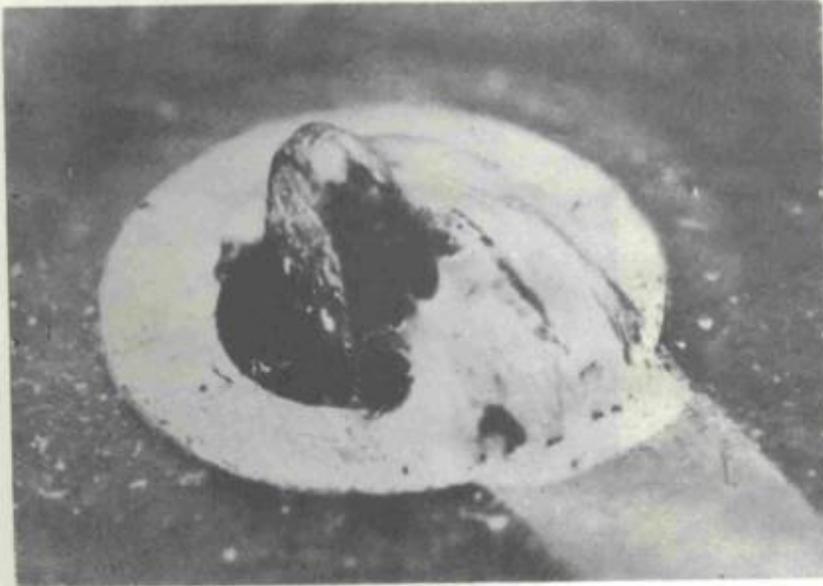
Exemplo de junta defeituosa mostrando desmolhagem da solda na placa e não-molhagem no terminal do componente.
